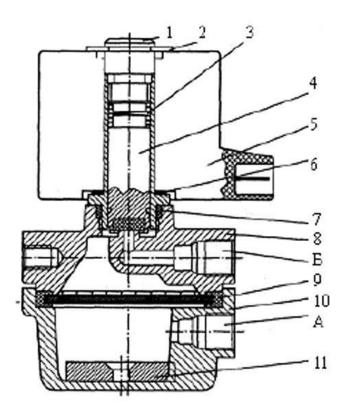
Электромагнитный газовый клапан: 1 - втулка направляющая; 2 - стопорная шайба; 3 - пружина: 4 - якорь: 5 - катушка: 6 - кольцо пружинное; 7 - кольцо уплотнительное; 5 - корпус; 9 - фильтр; 10- отстойник; 11 - магнит: А- вход газа; Б - выход газа
